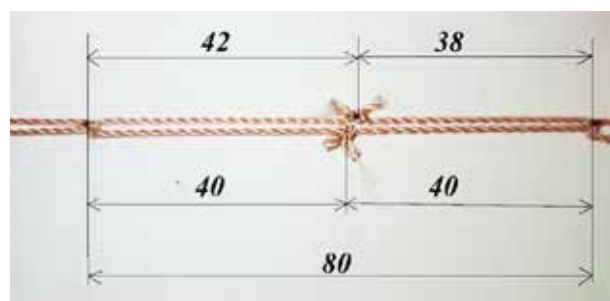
Измерение конструктивного и фабричного размера ячеи
